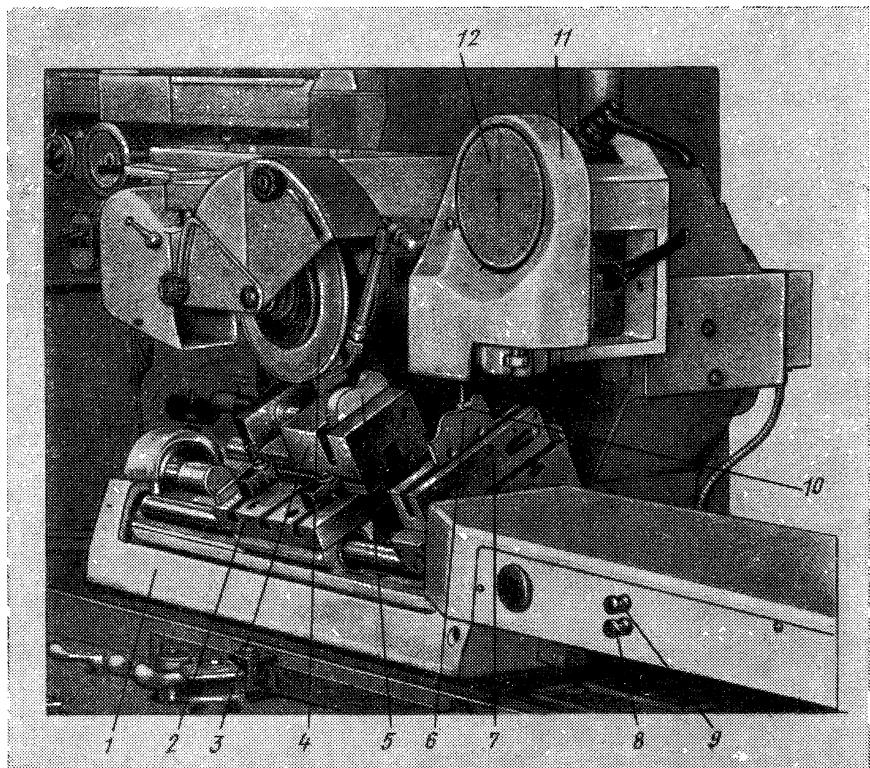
Устройство «Копиформ» к плоскошлифовальным станкам
